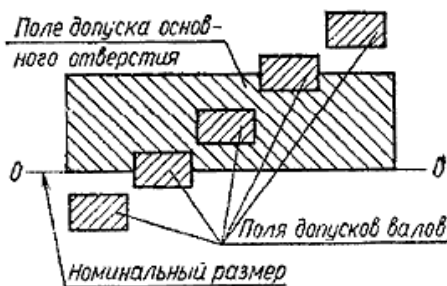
Схема расположения полей допусков посадки
